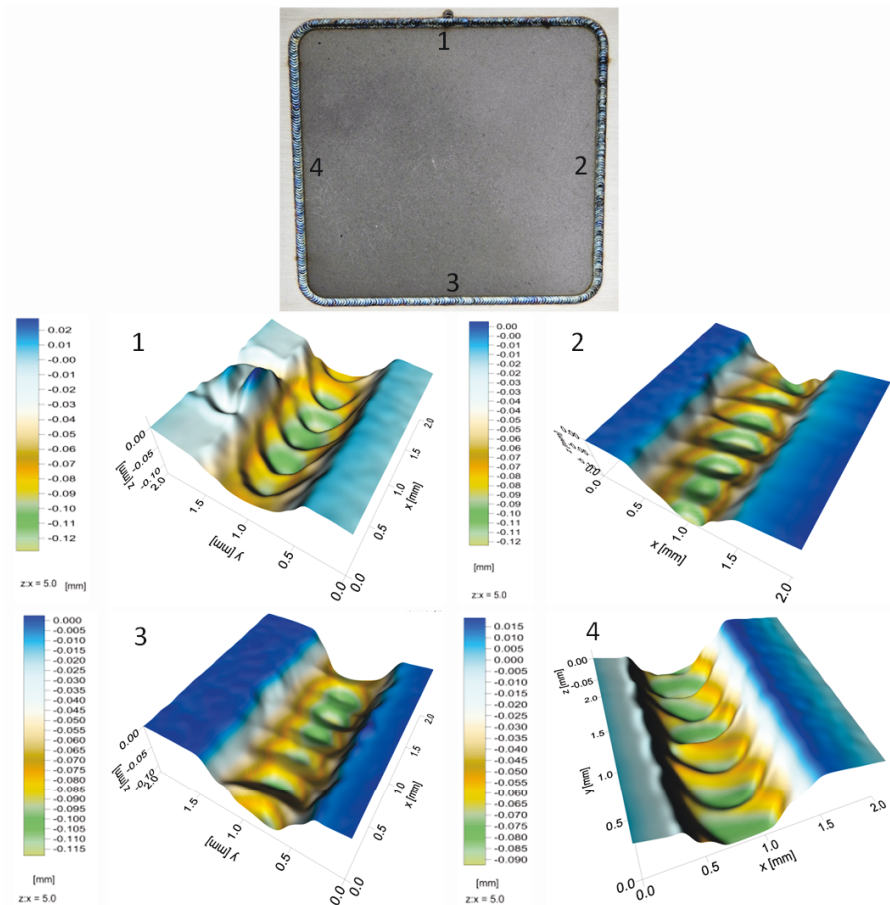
Einseitige Schweißnaht am Fensterblech TBM-D1a3-25-120x120-1100-3-13, Oberansicht.
